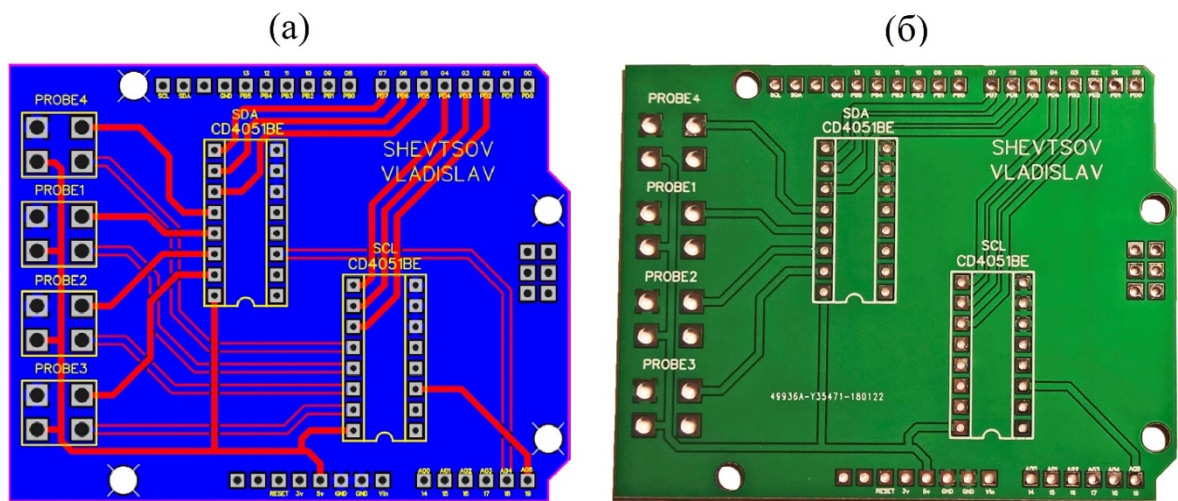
Макет (а) и готовый образец (б) печатной платы.
